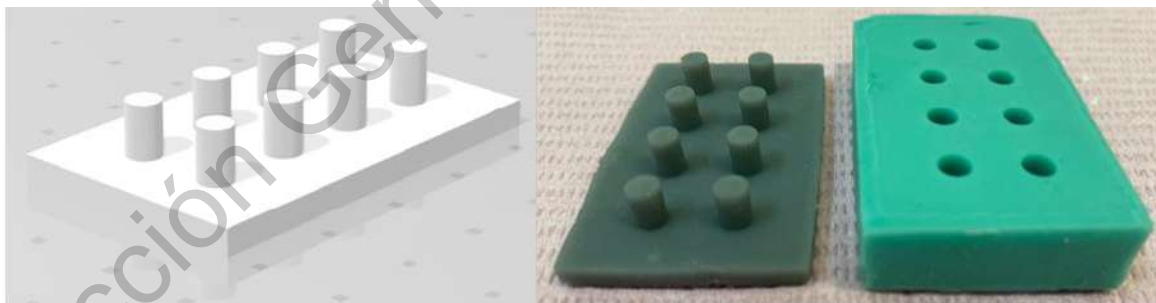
Elaboración de moldes: Diseño digital, Impresión 3D, Molde para realizar 8 muestras.
